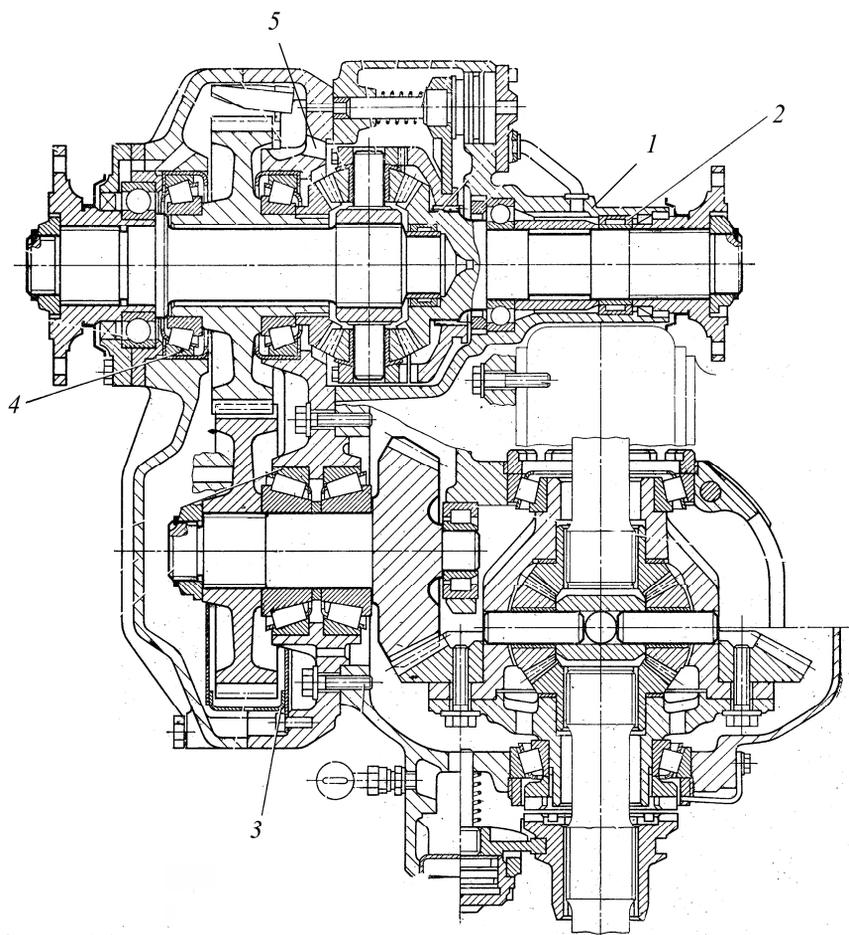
Проходной центральный редуктор автомобиля Магirus-290
